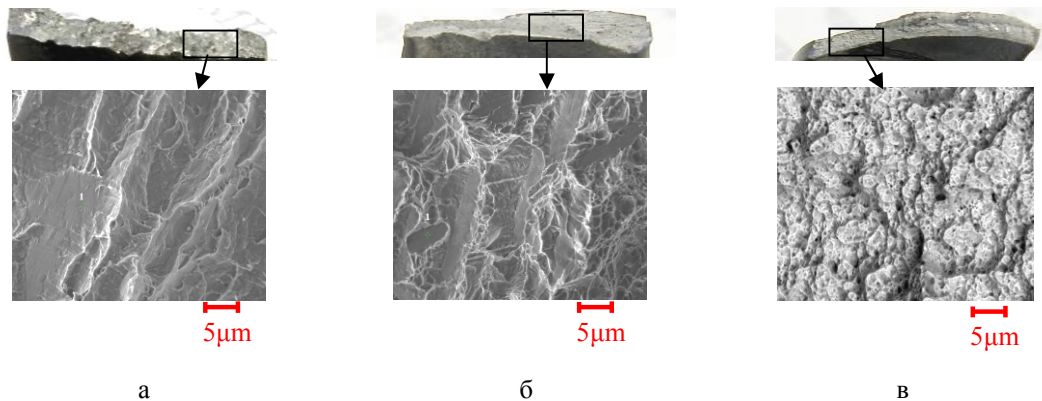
Типичные поверхности разрушения сварных образцов: а – АДС; б – ЭЛС; в – СТ
